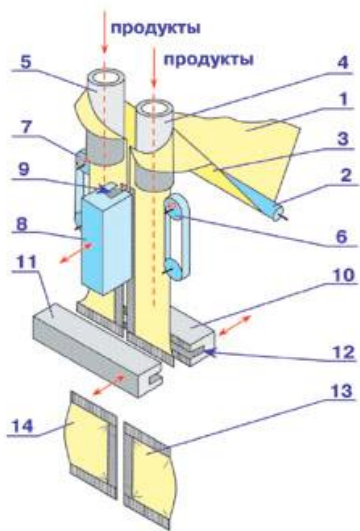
Компонування машини зі зпареними рукавоутворювачами: 1, 3 – плівка; 2 – механізм натягу плівки; 4, 5 – рукавоутворювачі; 6, 7 – механізми протягування плівки; 8 – губка поздовжнього зварювання; 9, 12 – відрізний механізм; 10 – губки поперечного зварювання; 13, 14 – готовий пакет
